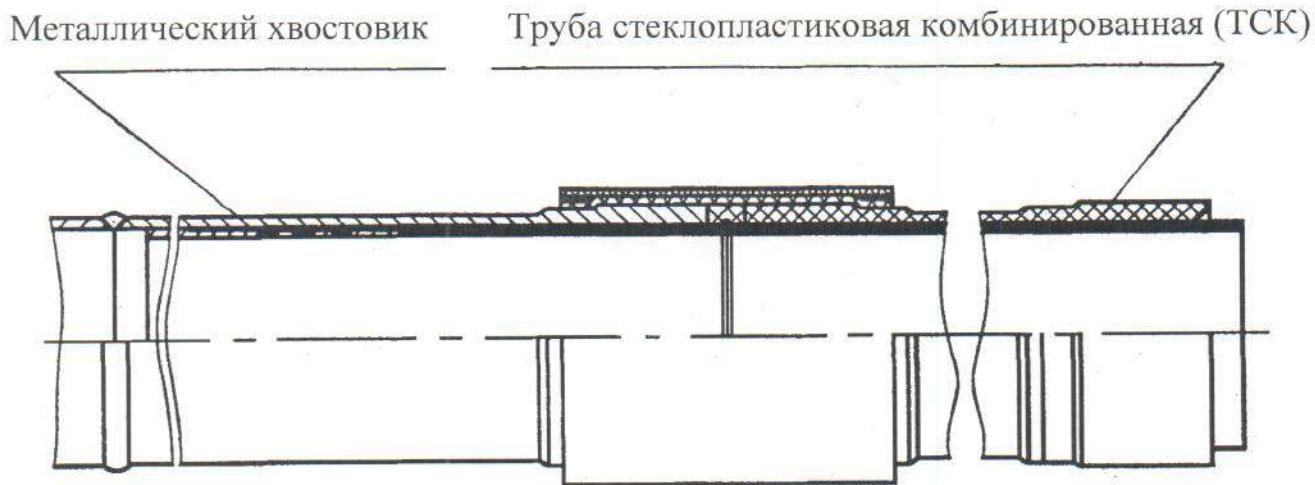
Переход стеклопластиковый комбинированный (ПСК) для сварного соединения со стальным трубопроводом
